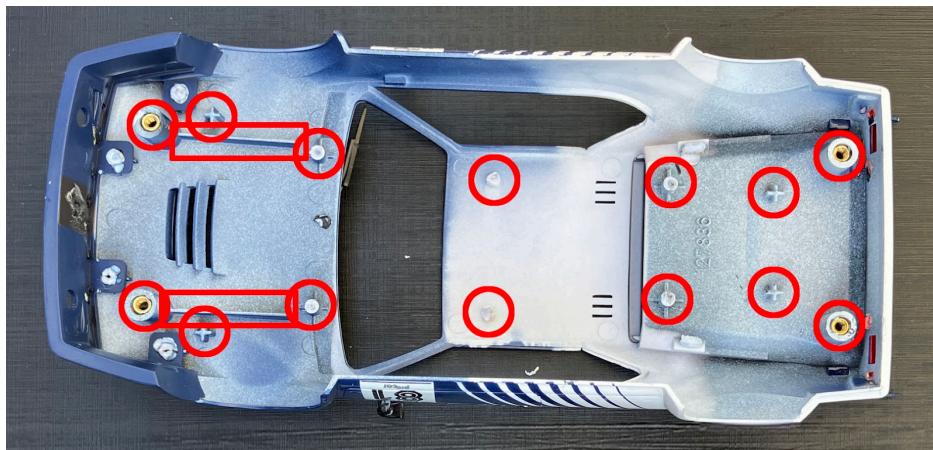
Befestigungspunkte der Carrera Interieurbauteile
